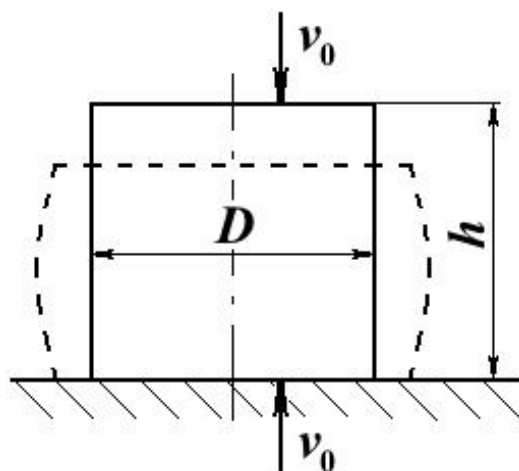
Схема процесу осадки циліндричної заготовки з тертям
